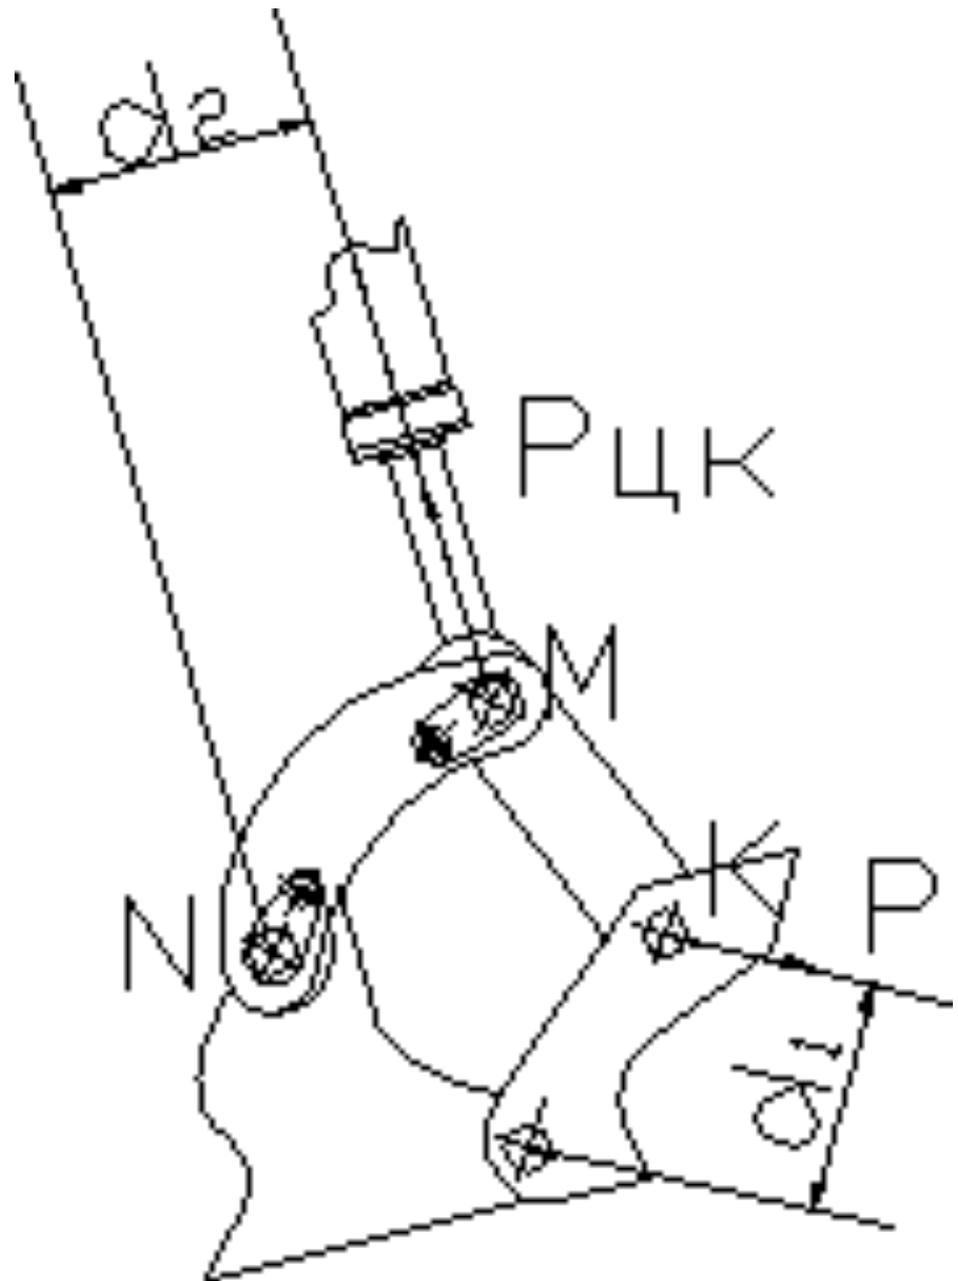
Расчетная схема для расчёта усилия в гидроцилиндре ковша (Аналогичное усилие будет и на втором ковше).
